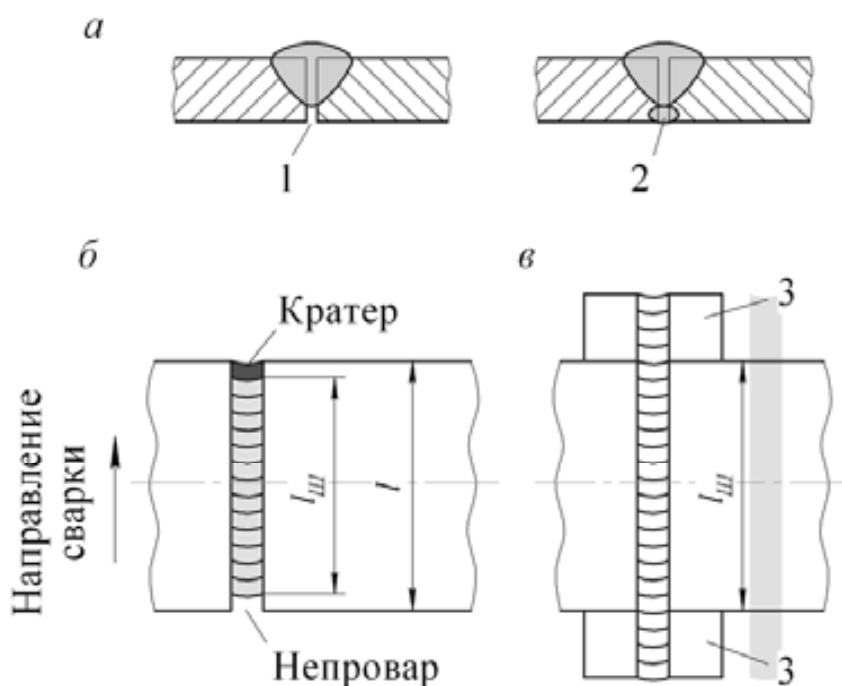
Выполнение сварных соединений: *а* – подварка корня шва; *б* – образование непровара и кратера шва; *в* – выполнение шва на технологических планках; 1 — непровар корня шва; 2 — подварка корня шва; 3 — технологические планки;  $l$  – длина шва;  $l_{ш}$  – расчетная длина шва
